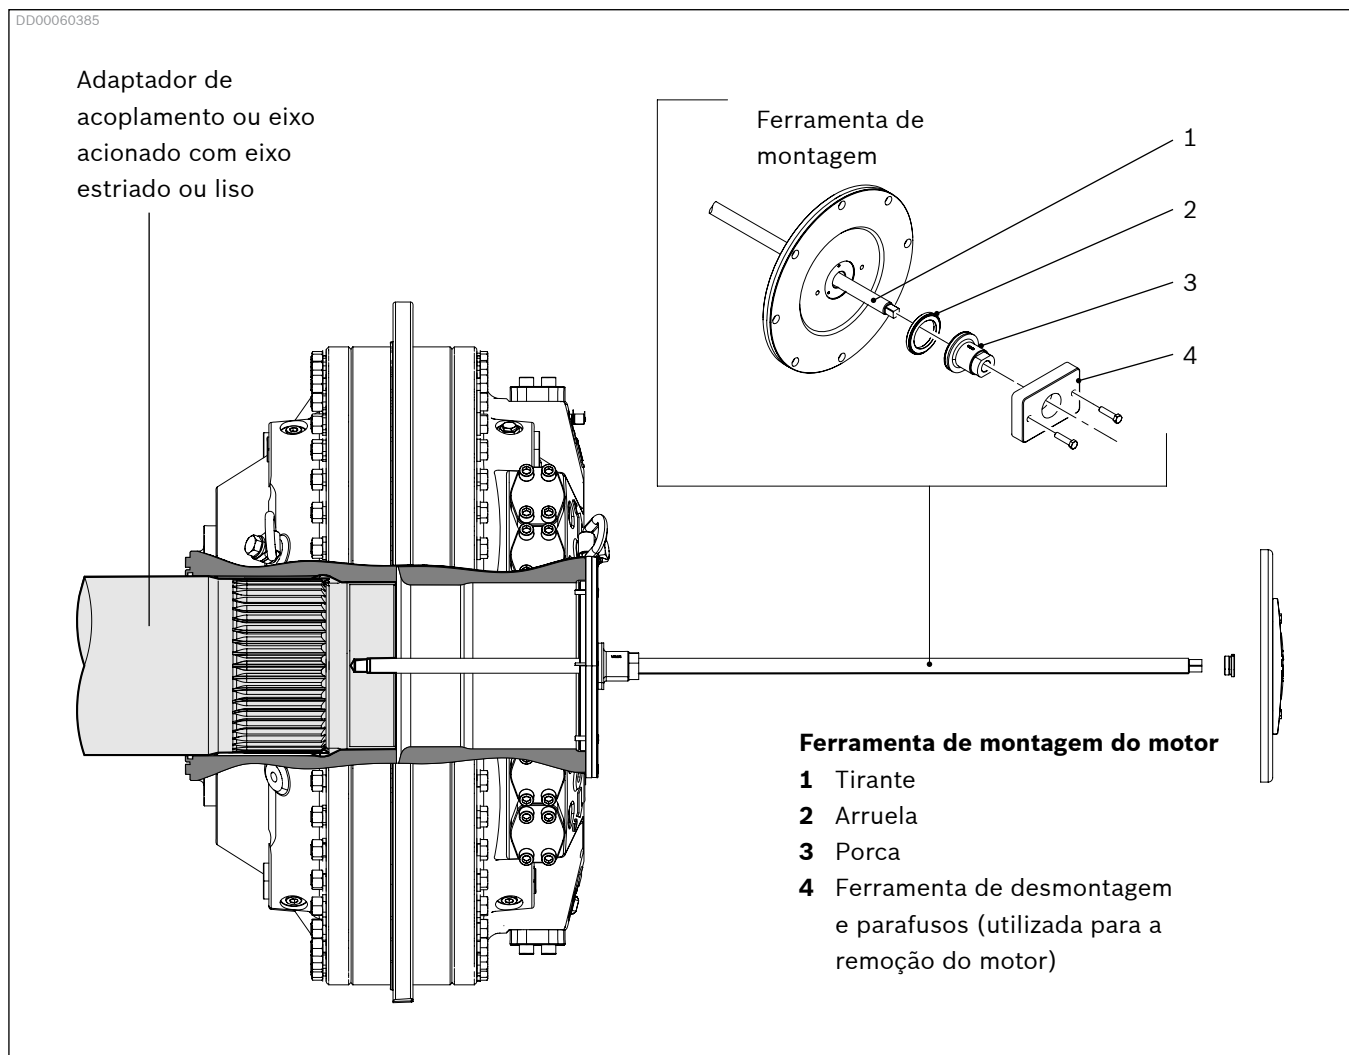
Montagem do motor CBm com a ferramenta de montagem
